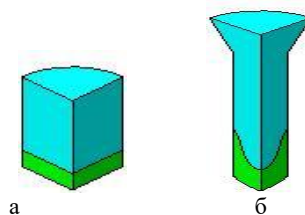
Заготовка із поперечною шаруватістю, отримана видавлюванням: а – вихідна заготовка; б - деталь
